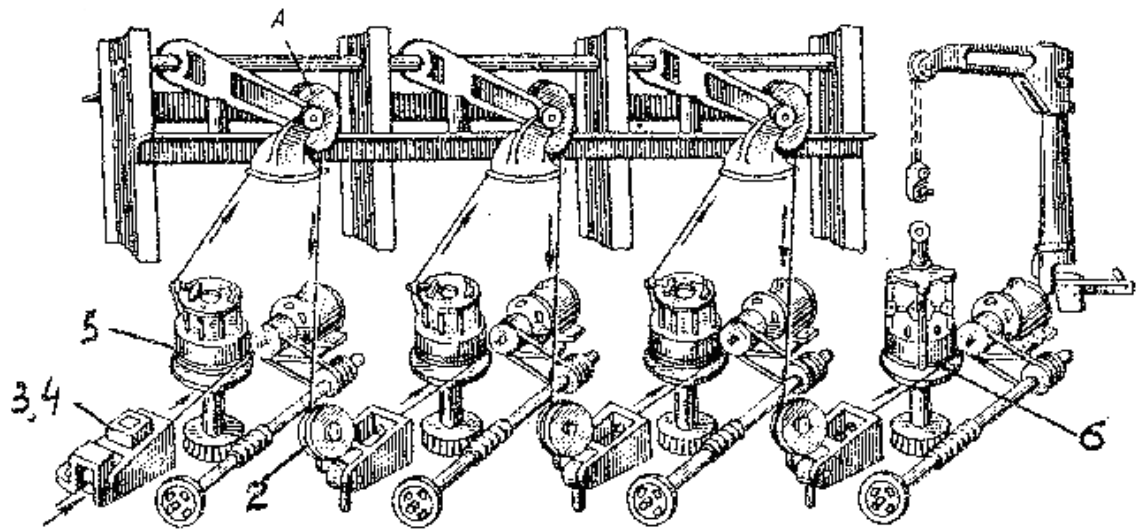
Схема стану багаторозового волочіння без ковзання: 1- бунт катанки; 2 - напрямний ролик; 3 - волокни; 4 - волокотримач; 5 - тягнучий барабан; 6 - тягнучий барабан для готового дроту
